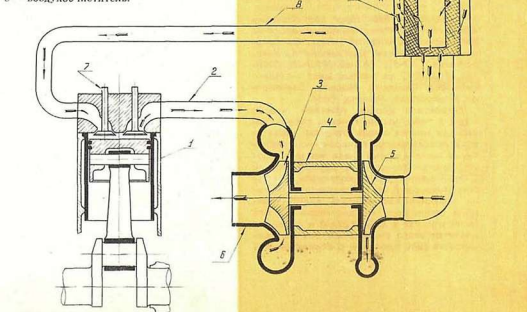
Схемы турбоагрегата в одноцилиндровом двигателе: 1 — цилиндр; 2 — выпускной коллектор; 3 — турбина; 4 — корпус турбоагрегата; 5 — центробежный компрессор; 6 — выпускная труба; 7 — впускной клапан; 8 — впускной трубопровод; 9 — воздухоочиститель.
